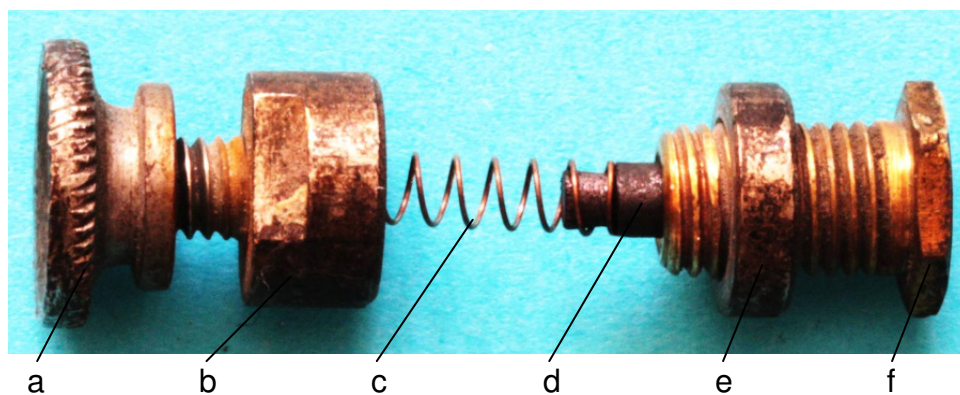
Kabelanschluss und Bürstenhalter: a) Rändelschraube, b) Überwurfmutter mit Gewindebolzen, c) Bürstenfeder, d) Kohlebürste, e) Mutter außerhalb des Gehäuses, f) Bürstenhalter (Gewinderohr mit Sechskantfläche innerhalb des Gehäuses)
